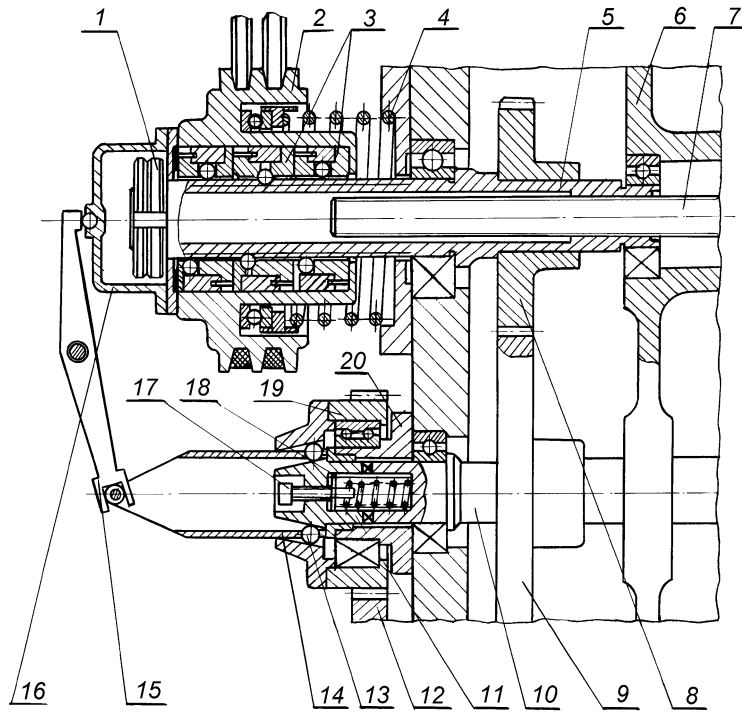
Схема автоматичного регулювання приводів подачі верстатів
